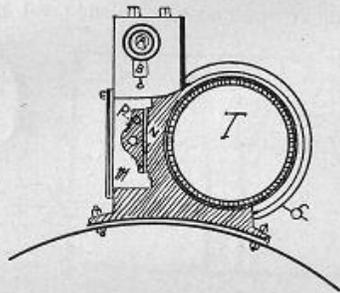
Cassetto della distribuzione del vapore, il cilindro e lo stantuffo - Sezione trasversale.
